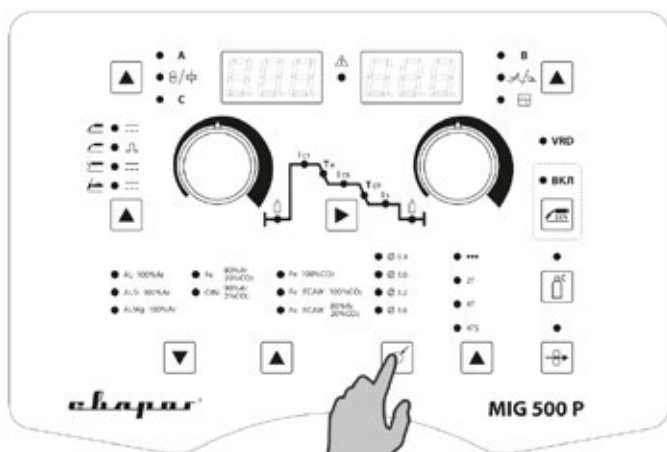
Выбор диаметра сварочной проволоки.
